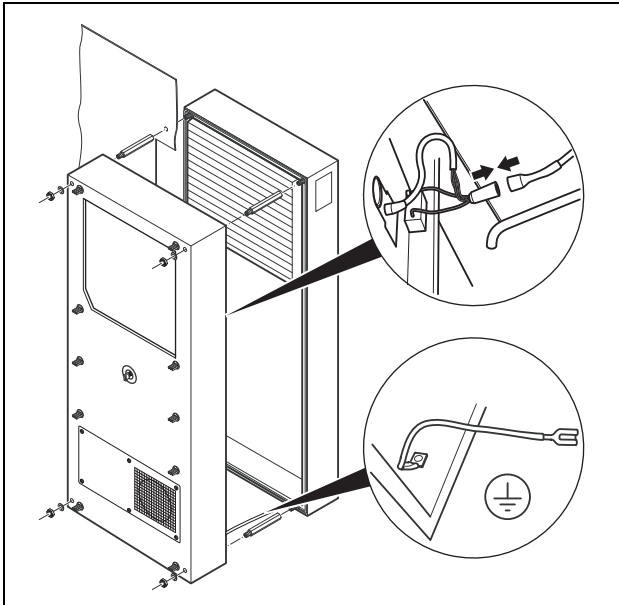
Крепление корпуса кондиционера в монтажный вырез и установка кожуха
